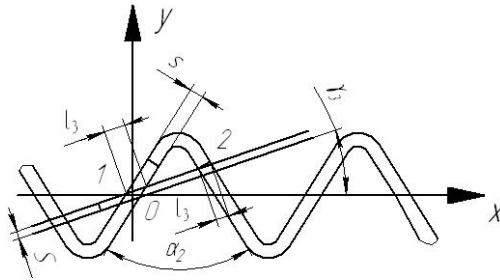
Розрахункова схема розточування внутрішнього діаметра профільної гвинтової заготовки прохідним різцем
